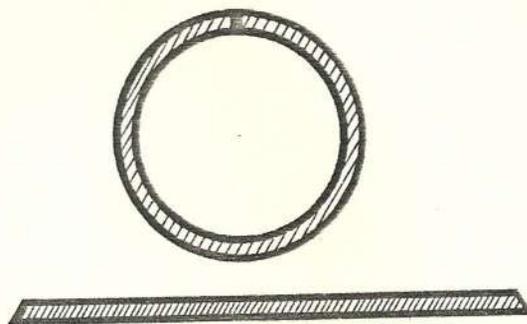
Pasos seguidos para fabricación de tubería al horno con traslape.
